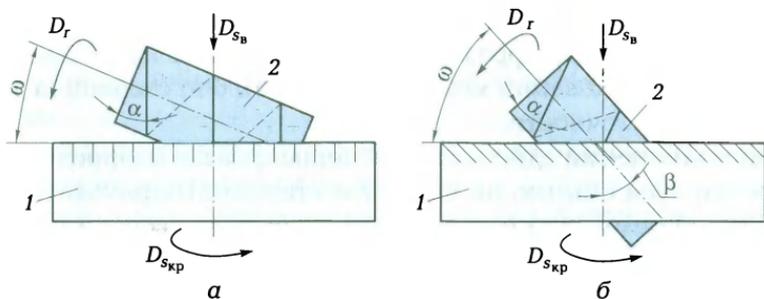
Схемы нарезания червячной фрезой цилиндрических колес с прямыми (а) и косым (б) зубьями:
